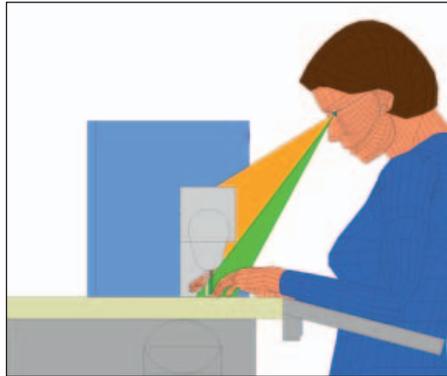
Eingeschränkte Einsehbarkeit des Näh- und Wirkbereichs, insbesondere hinter Nadel und Nähmaschine infolge Sichtfeldabdeckung durch Nähmaschinenarm
